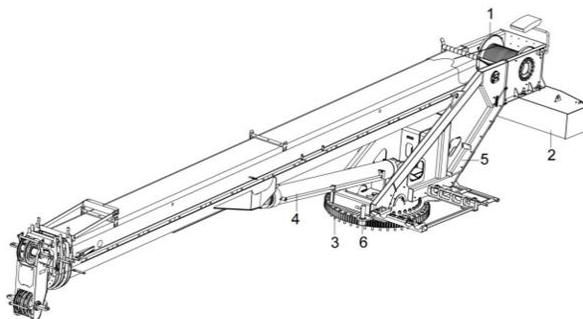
9. 11. 3 Загальний вид поворотної платформи:
